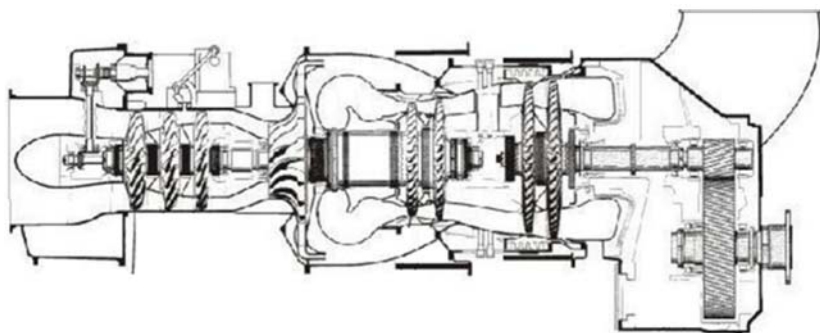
Схема двигателя Makila с редуктором, включенным в конструкцию двигателя, приводимым от ротора свободной турбины и расположенным сзади
